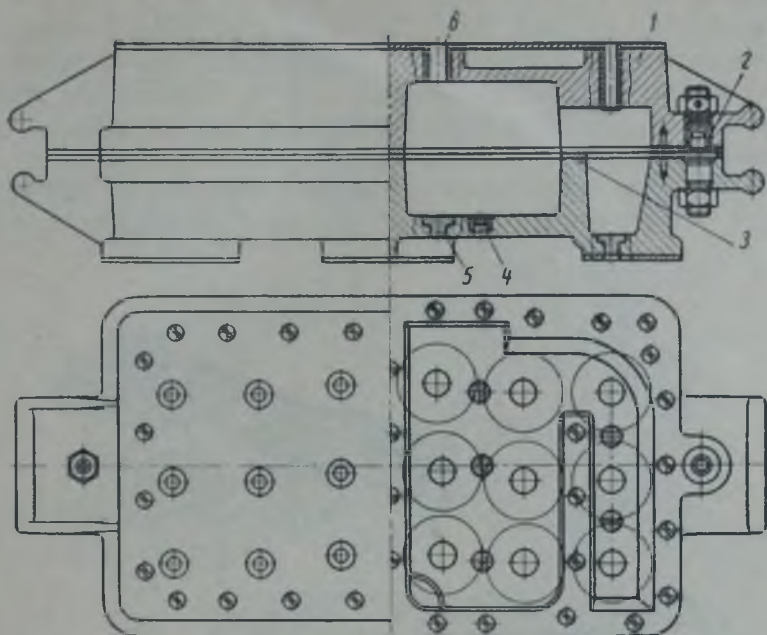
Металлический ящик для изготовления стержня на пескодувной машине:
